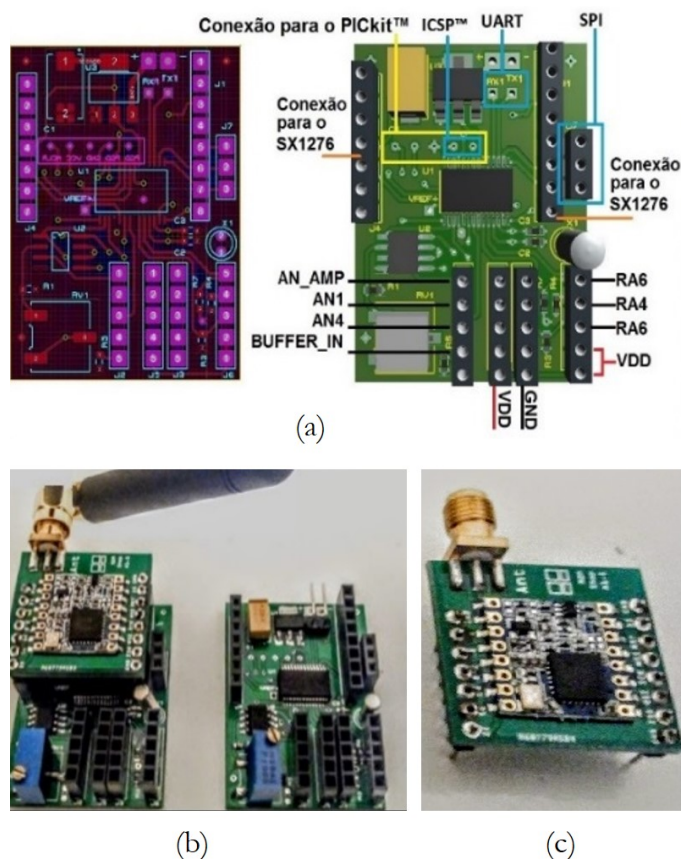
Confeção dos nós LoRaWAN (a) projeto PCB (b) montagem PCB + circuito montado (c) módulo SX1276.
